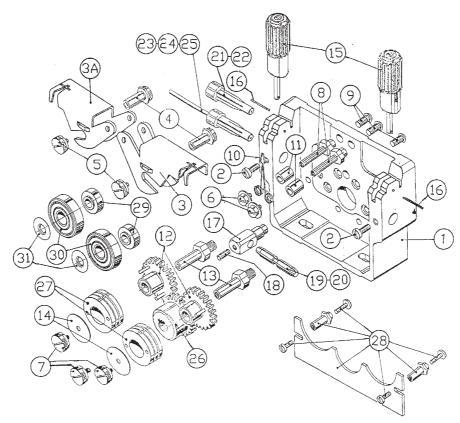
/6а. 4-роликовый механизм подачи сварочной проволоки. Изображение в разобранном виде / exploded view wire feed 4-rolls drive
